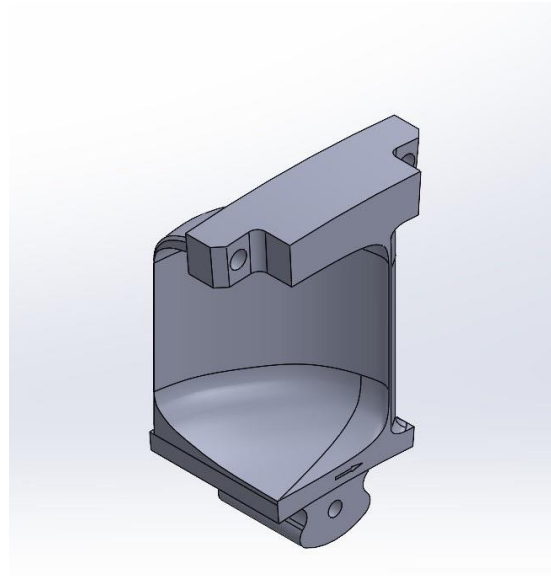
斜衝擊式 Turgo 單葉片 CAD 圖 [24]
